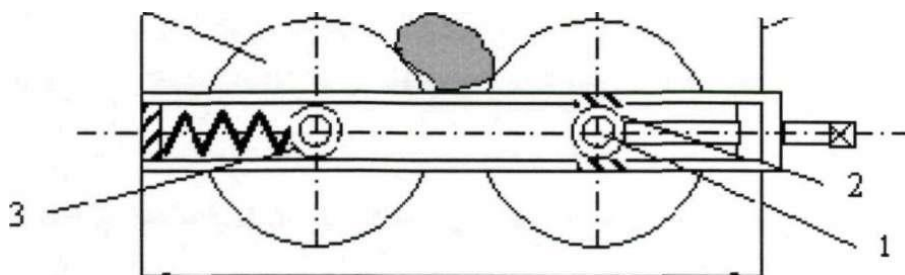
Схема двухвалковой дробилки с гладкими валиками
